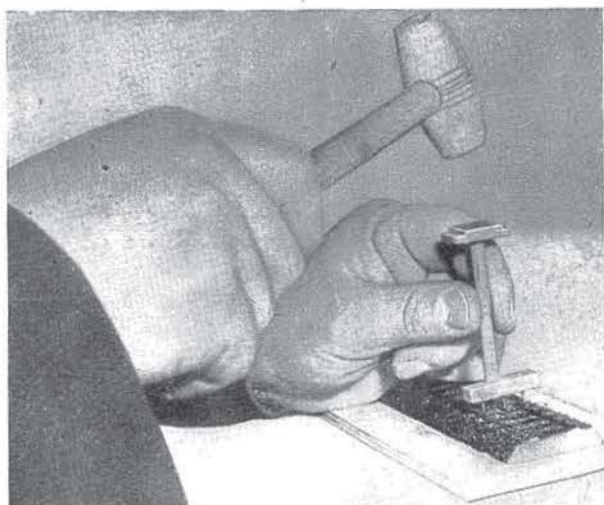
Vorstechen der Löcher für die Befestigungsplättchen.
